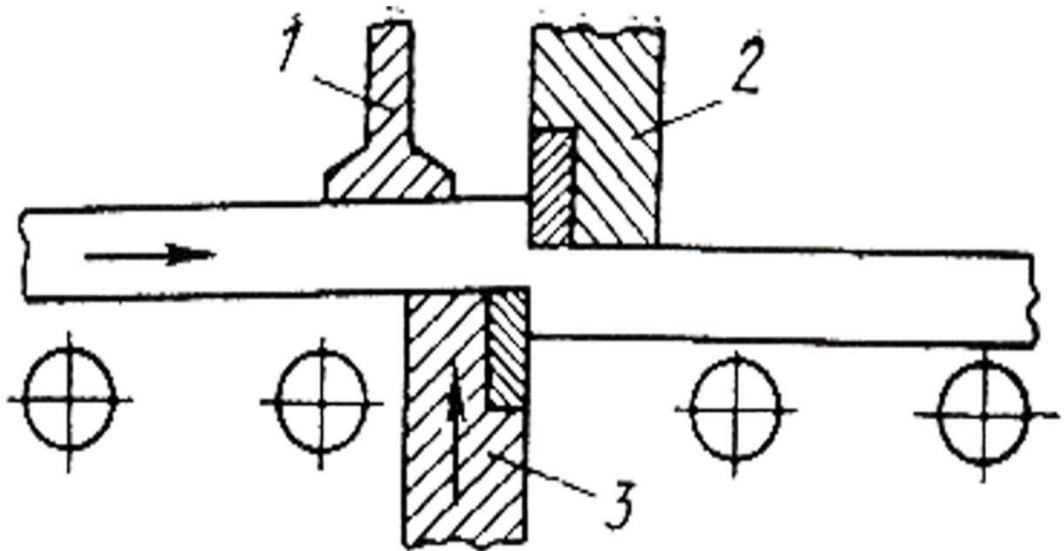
Схема різання металу на ножицях зусиллям 900т.
